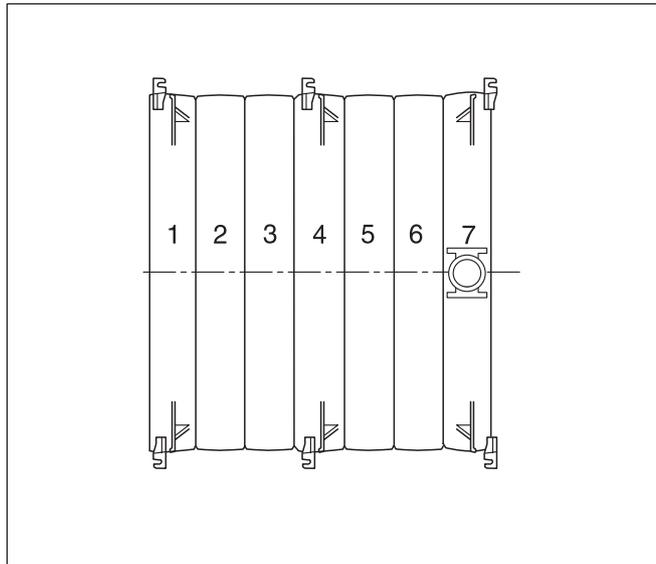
Draufsicht: Kesselblock (7 Kesselglieder) mit Konsolen
